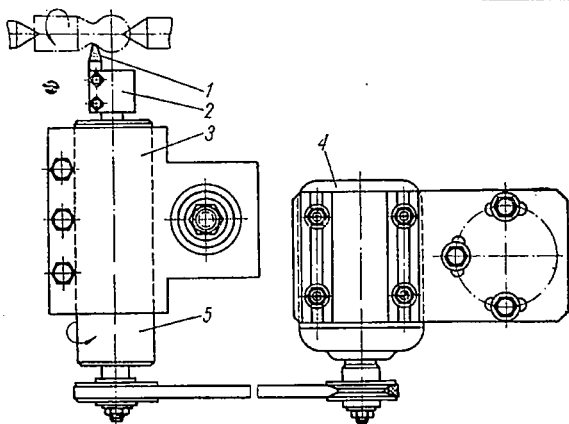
Приспособление для обработки сферических поверхностей вращающимся резцом.
